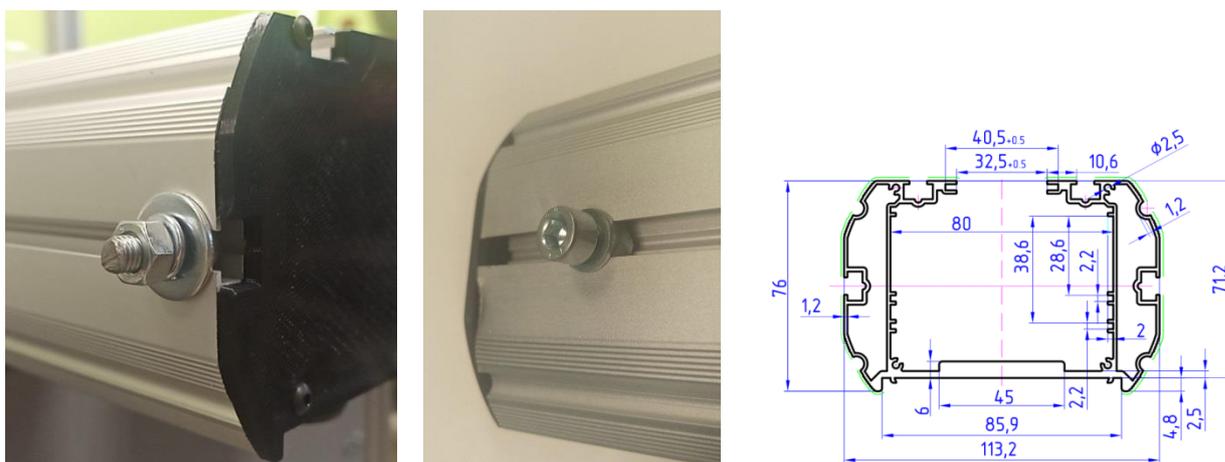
а), б) способы крепления модуля, в) размеры корпуса в сечении
